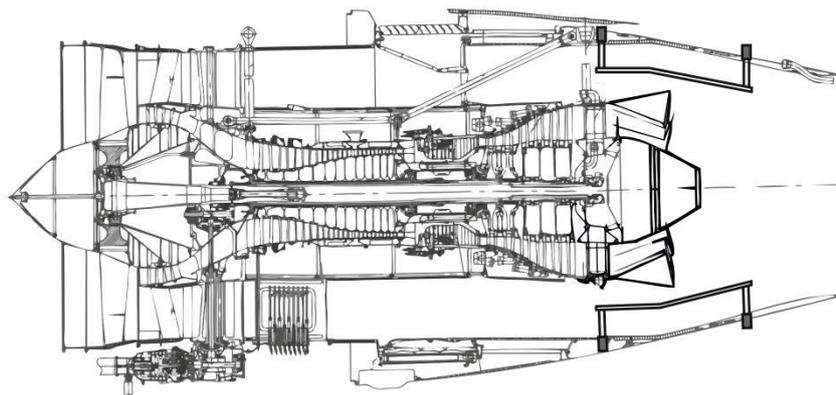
Схема установки предлагаемого устройства в камере смещения ТРДД в рабочем положении
